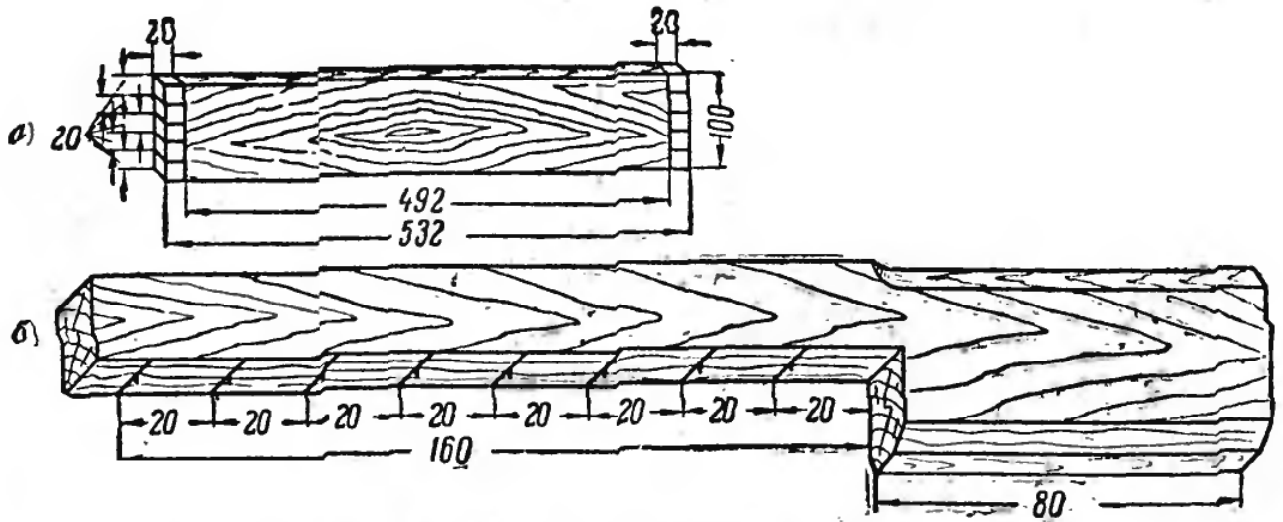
Разметка прямых шипов гребёночным рейсмусом:
